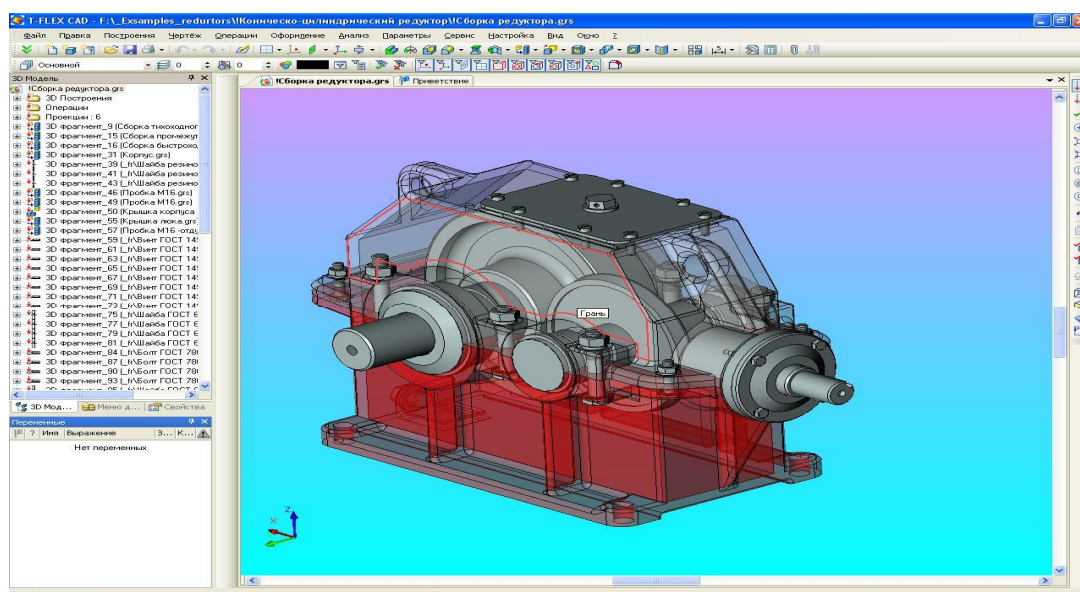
Компьютерный тренажер коническо-цилиндрического редуктора реализованный при помощи CAD – системы T-FLEX
